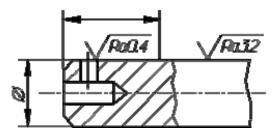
Пример обозначения различной шероховатости на одной поверхности
